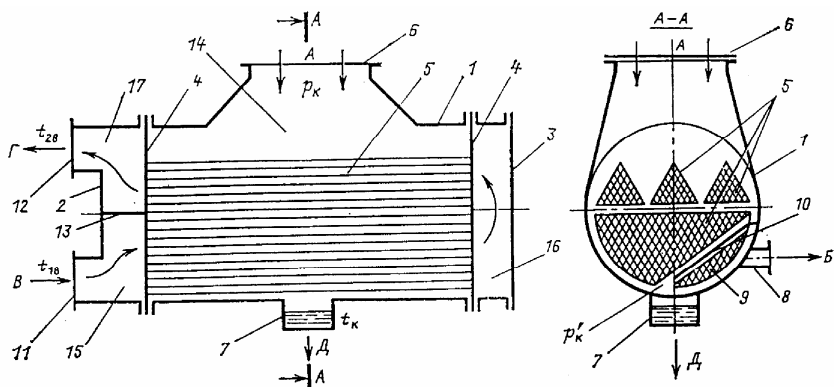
Схема двухходового поверхностного конденсатора: 1 – корпус конденсатора, 2,3 – крышки водяных камер, 4 – трубная доска, 5 – конденсаторные трубки, 6 – приемный паровой патрубок, 7 – конденсатосборник, 8 – патрубок отсоса паровоздушной смеси, 9 – воздухоохладитель, 10 – паронаправляющий щит, 11 – входной патрубок, 12 – выходной патрубок для воды, 13 – разделительная перегородка, 14 – паровое пространство конденсатора, 15-17 – входная, поворотная и выходная камера охлаждающей воды, А – вход отработавшего пара, Б – отсос паровоздушной смеси, В,Г – вход и выход охлаждающей воды, Д – отвод конденсата.
